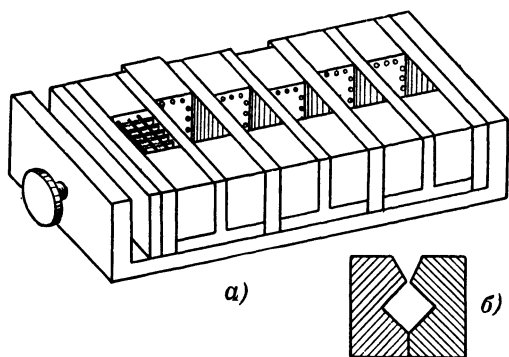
Приспособление для заливки микромодуля (а) и схема заливки с ребра (б).
